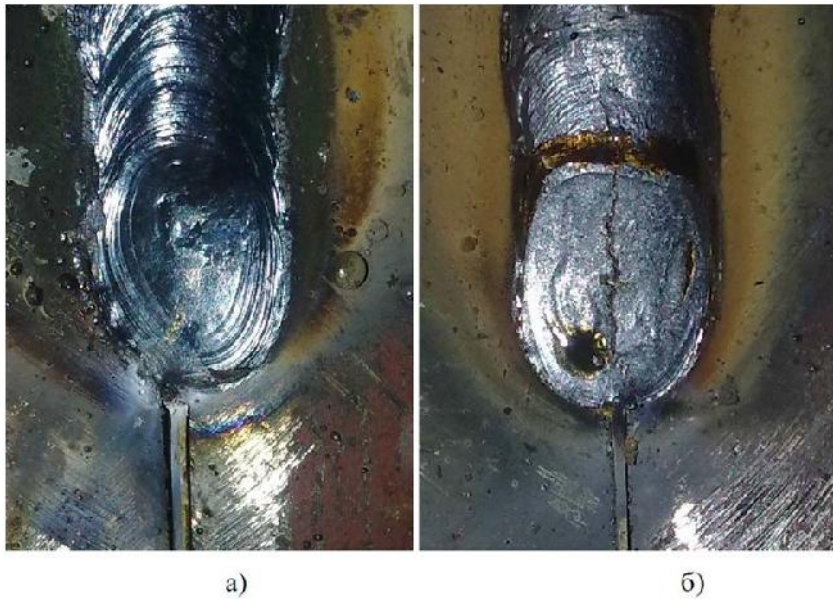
Кратер сварного шва: а) ручной дуговой сварки; б) полуавтоматической в среде CO₂.
